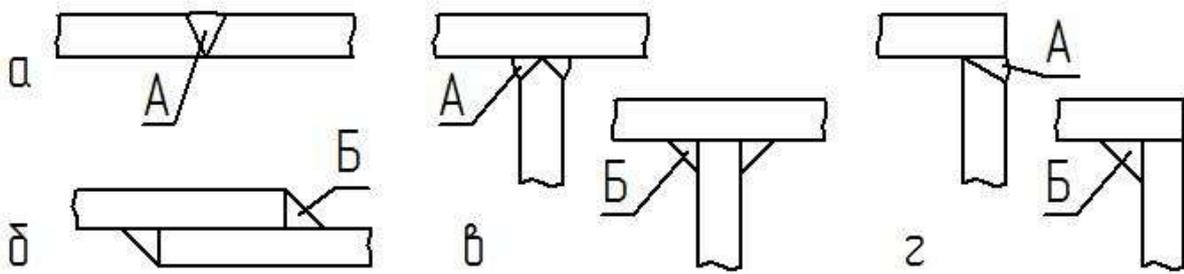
Види зварних з'єднань і типи зварних швів
